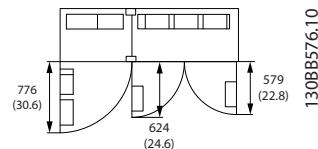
Пространство перед корпусом типа IP21/IP54, типоразмер F12
